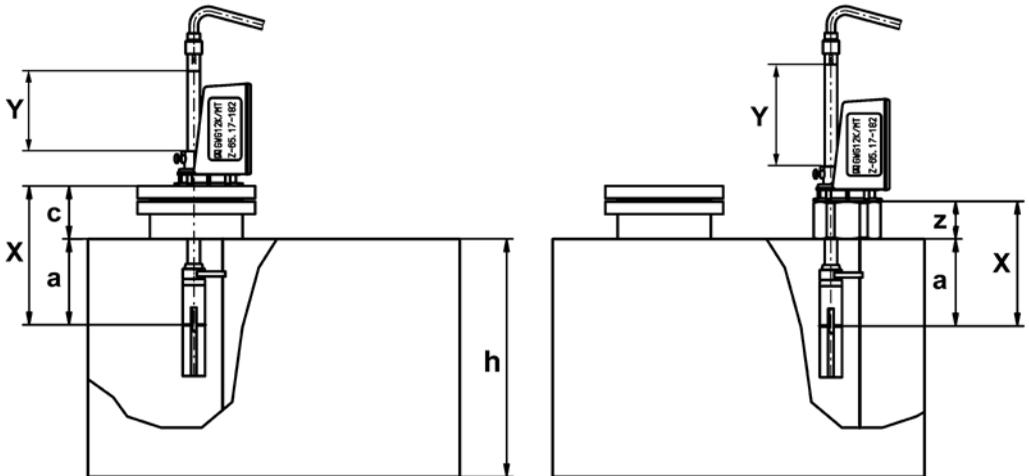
Einbau auf Domdeckel (links), Einbau auf Tankdeckel (rechts)
